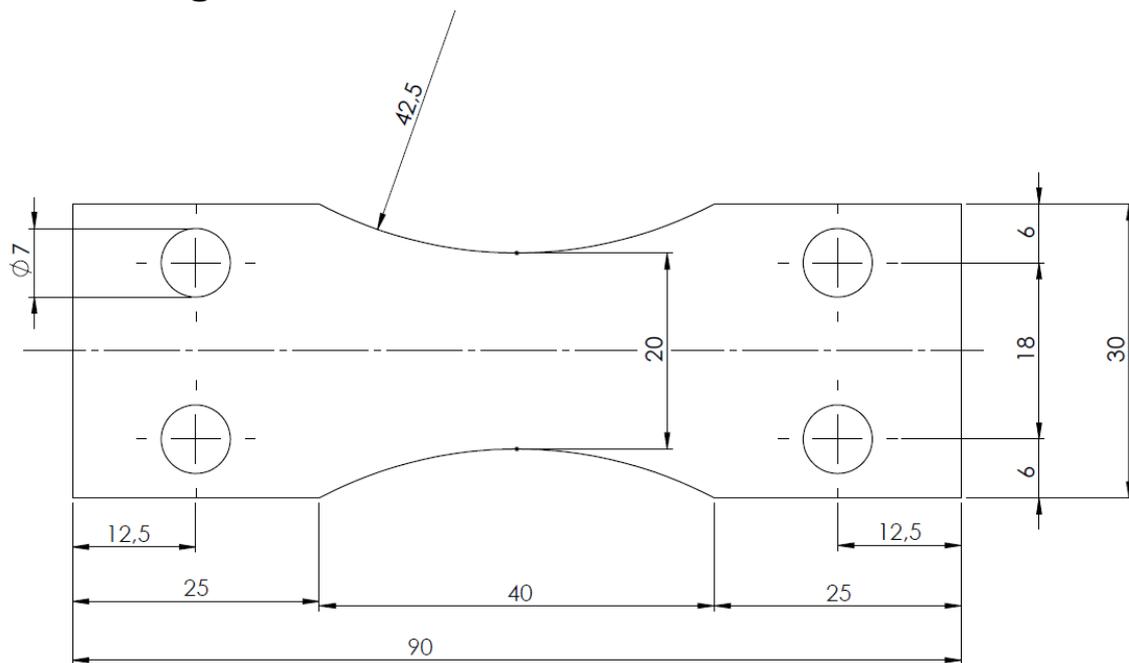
Probenform für Wechselbiegemaschine ohne Loch, Probendicke 3mm
